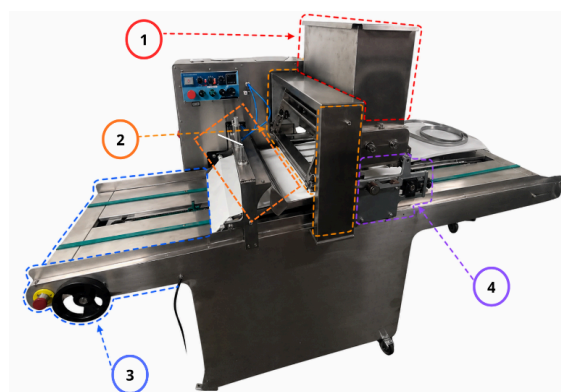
Destaque das partes móveis que devem ser enclausuradas.
